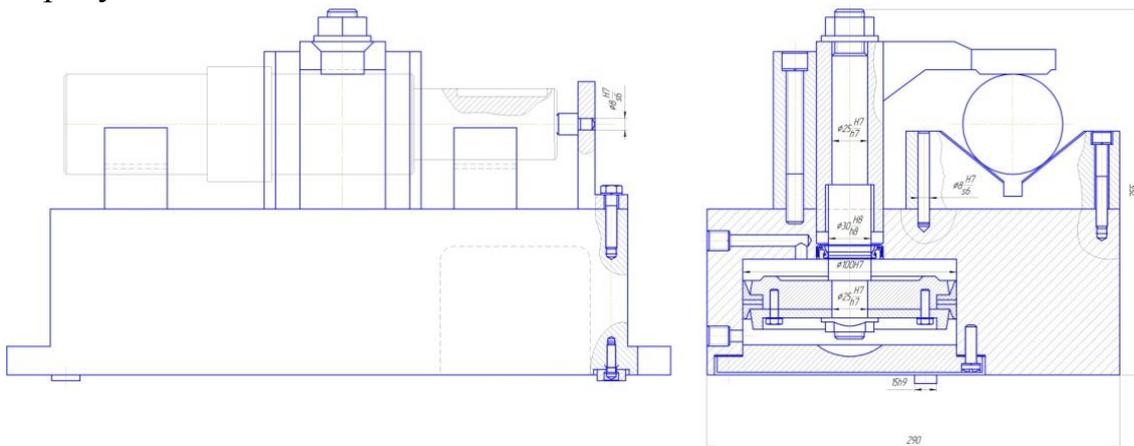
Схема установки и закрепления детали в приспособлении
